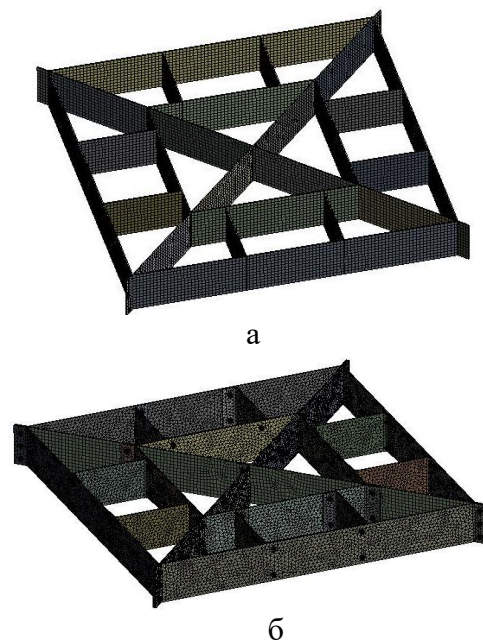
Конечно-элементные модели металлоконструкций грузовых тележек с универсальной компоновочной схемой: а – модель металлоконструкции со сварными соединениями; б – модель металлоконструкции с болтовыми соединениями
